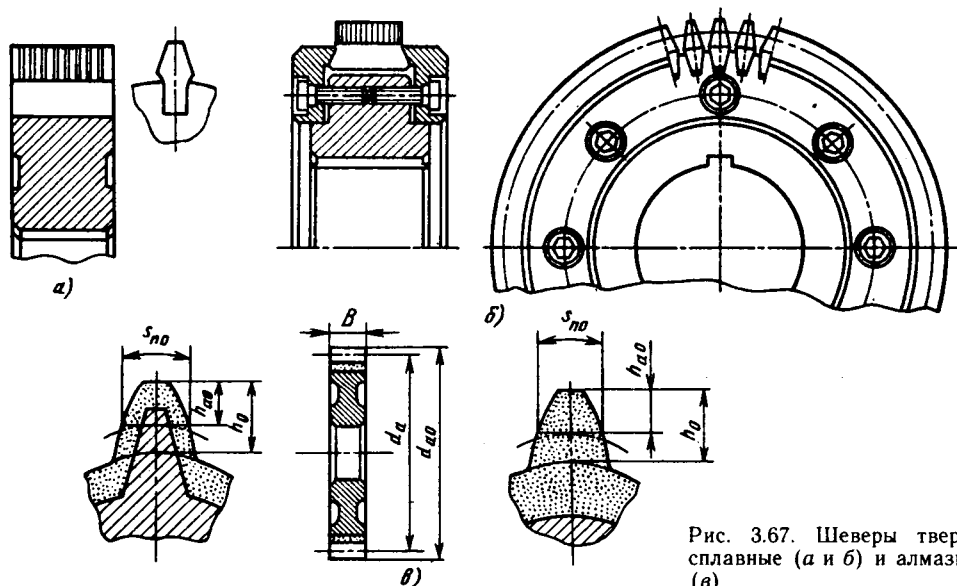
Шеверы твердосплавные (а и б) и алмазные (в)
